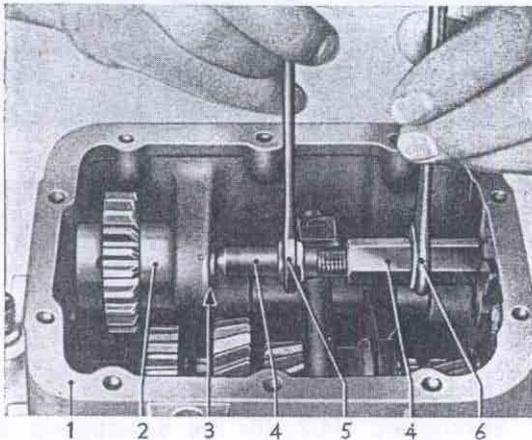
Achse für Rücklauf­rad mit Ausdruckschraube SW-208 aus Getriebegehäuse herausdrücken
